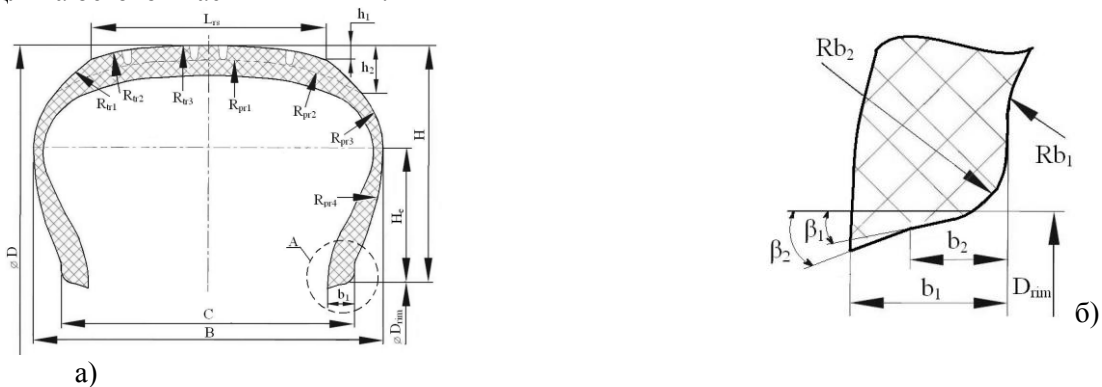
Геометрическая модель профиля поперечного сечения пневматической шины и его основные размеры а) – профиль шины; б) – борт
